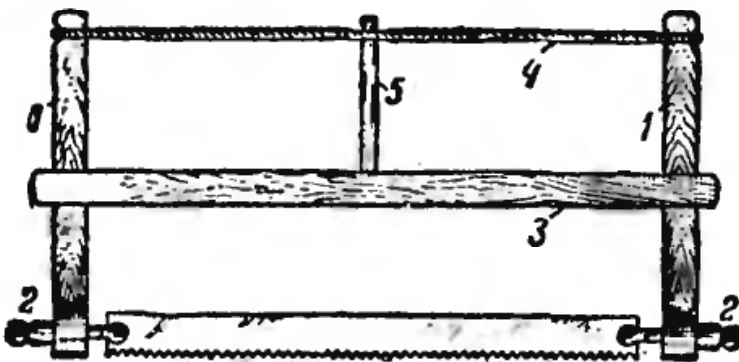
Лучковая пила: 1 — стойки деревянные с утолщением и отверстиями в них для ручек; 2 — ручки с пропилами для закрепления полотна пилы; 3 — распорная планка с гнездами для стоек; 4 — тетива — шнур, пеньковый шпагат для натяжения полотна пилы; 5 — закрутка.
